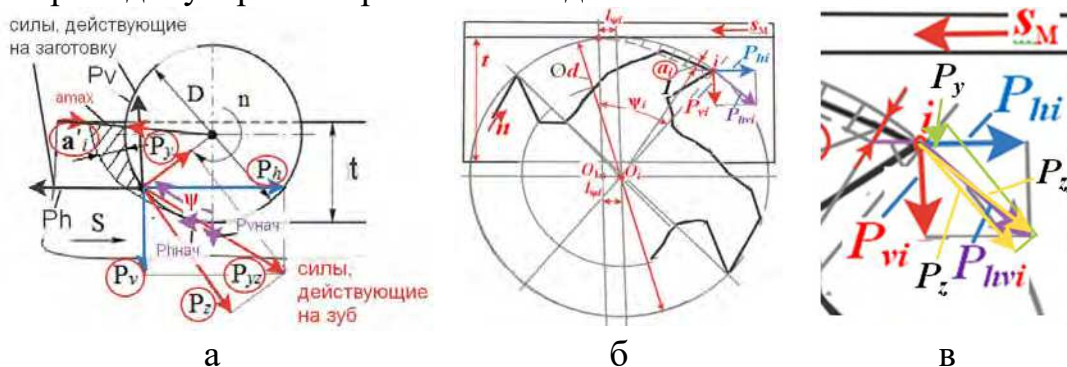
Схема направления составляющих силы резания при несимметричном встречном концевом фрезеровании: а – при положении фрезы после заготовки на виде сверху; б – при положении фрезы перед заготовкой на виде сверху, как в рассматриваемом эксперименте; в – схема действия составляющих P_{vi} и P_{li} , а также P_z и P_y и их результирующих P_{hvi} и P_{zy}
